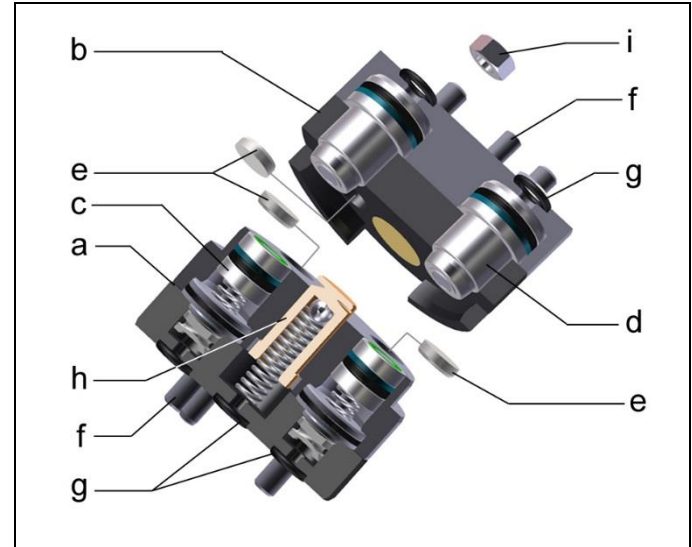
Construction - sous-ensemble femelle et sous-ensemble mâle
